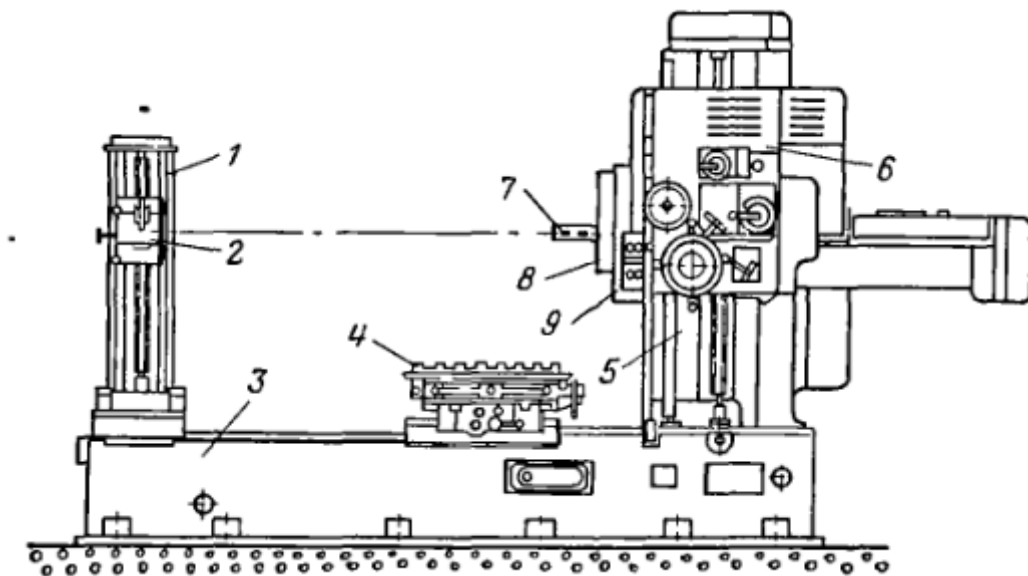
Загальний вид горизонтально-розточного верстату
